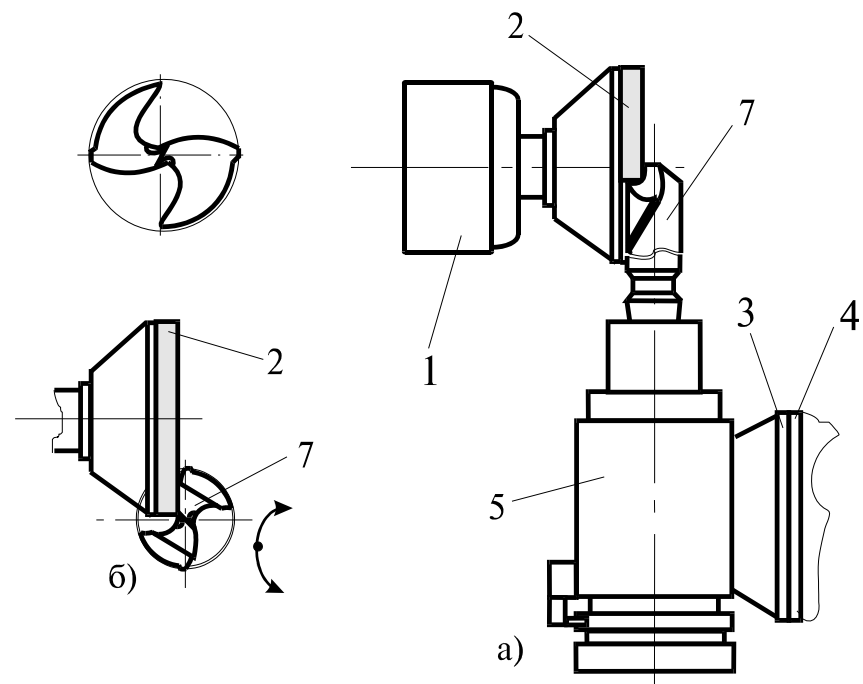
Схема заточки переднего угла  $\gamma$  по плоскости  $A\gamma$  (а) и подточки перемычки (б). 1 – Станок; 2 – Шлифовальный круг; 3 и 4 – Кронштейны приспособления; 5 – Делительная головка; 6, 7 – Сверло.
